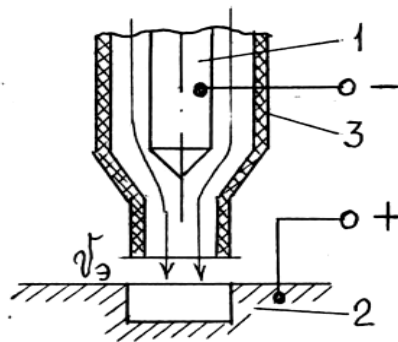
Схема прошивання струменевим методом: 1 – електрод-інструмент (струмопровід); 2 – заготовка; 3 – діелектричний корпус
